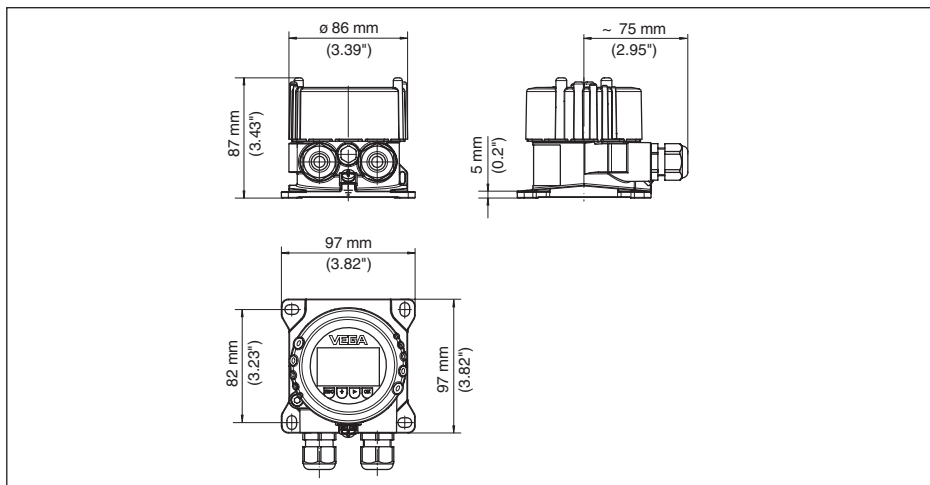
VEGADIS 82 с корпусом из нержавеющей стали (точное литье)
